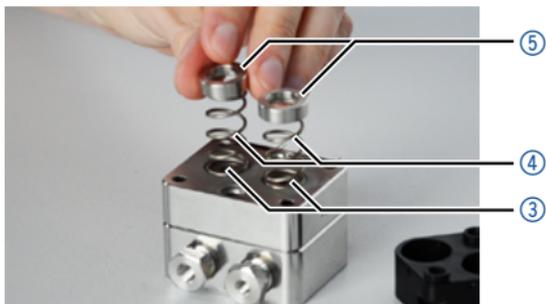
Zusammenbau der Komponenten der Kolbenführung
